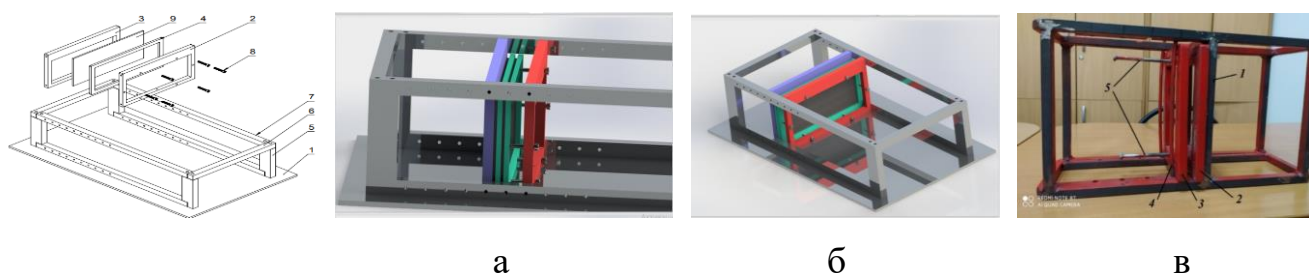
Зажимное приспособление для крепления образцов для испытаний на удар: а – чертеж, б – 3d модель, в – готовое изделие
